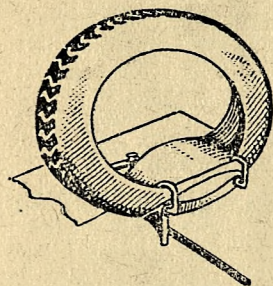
Укрепляемое на верстаке простое приспособление для разжимания бортов легкой покрышки
